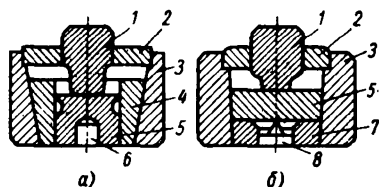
Выдавливание: а — с облегчающей камерой; б — с приемником; 1 — мастер-пуансон; 2 — направляющее кольцо; 3 — обойма; 4 — разрезное кольцо; 5 — заготовка; 6 — облегчающая камера (полость в заготовке); 7 — приемник; 8 — центр
